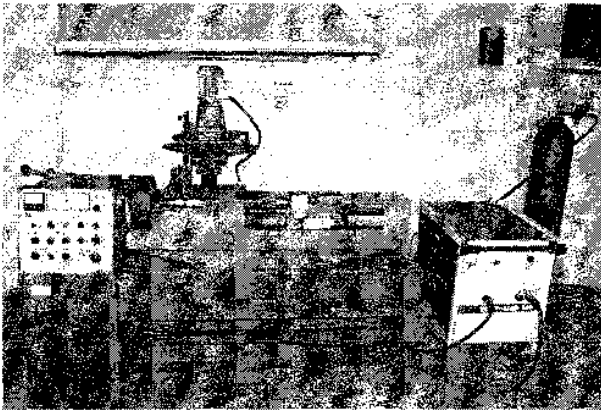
Установка для наплавлення шийок колінчастого вала в середовищі захисних газів.
